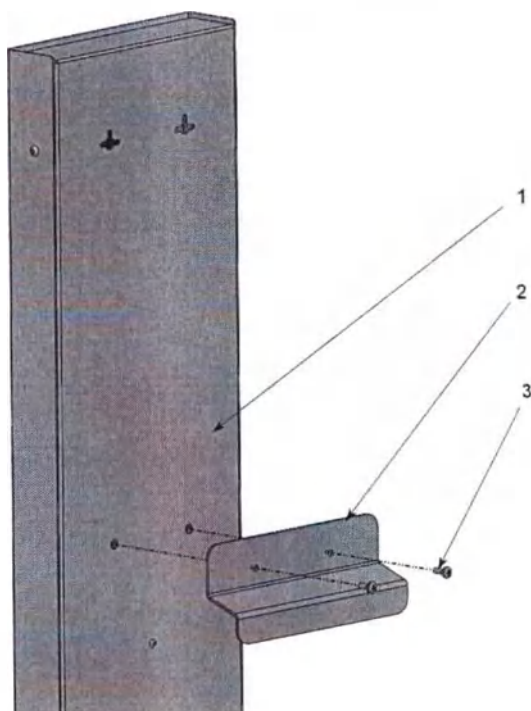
Монтаж ручки облучателя серии РВ. 1- Облучатель; 2- Ручка; 3- Винт М4.
